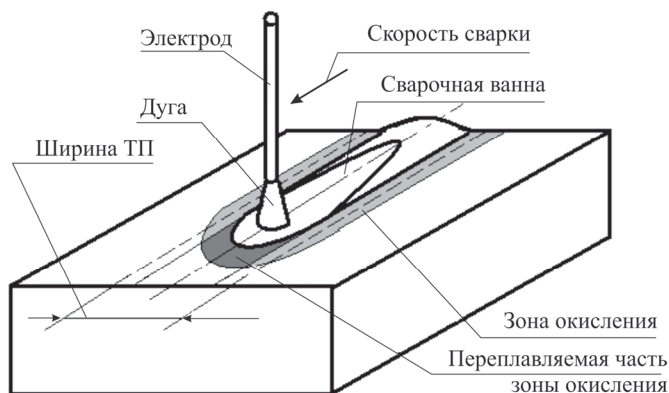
Расположение зоны окисления при дуговой сварке.
